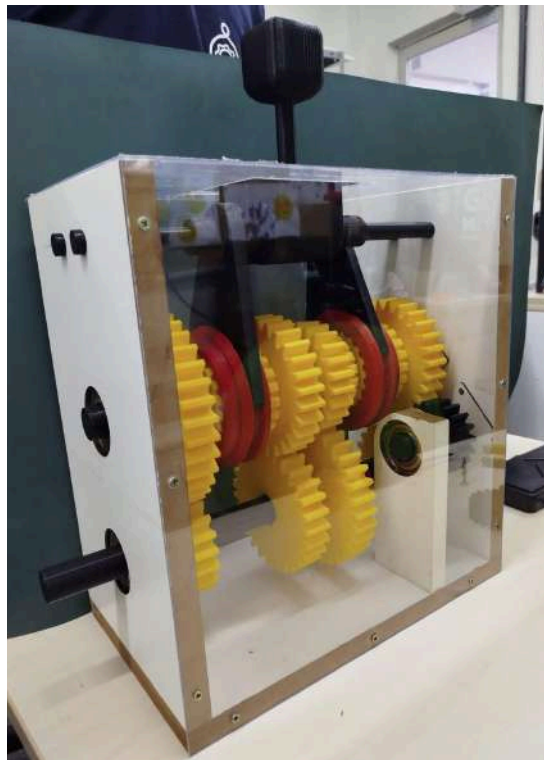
Montagem das engrenagens e mecanismos de seleção de marchas
